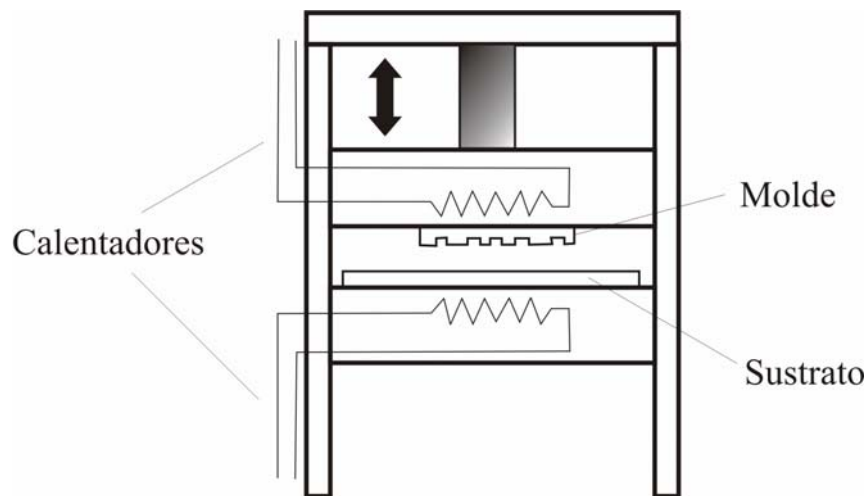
Dispositivo experimental para el estampado del patrón del molde mediante *hot embossing*.
